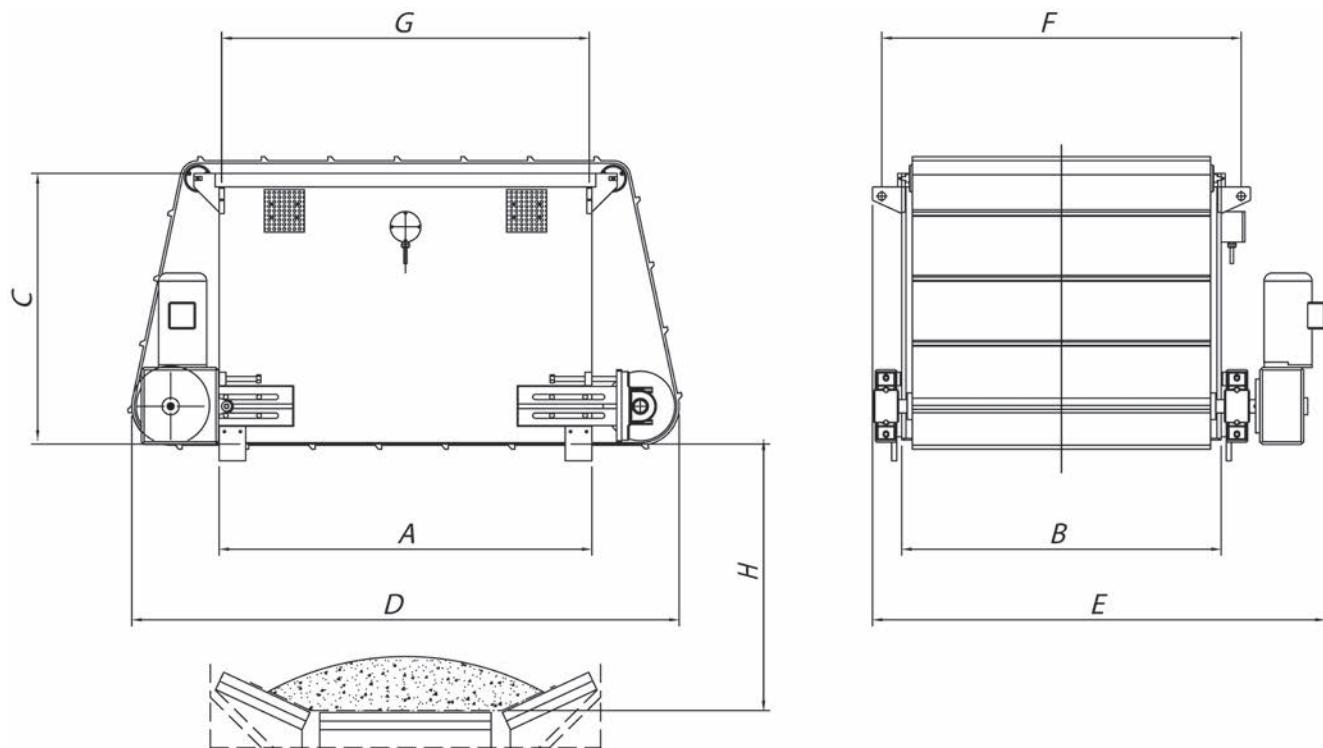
dimensões principais dos separadores eletromagnéticos *air cooled* de limpeza automática
